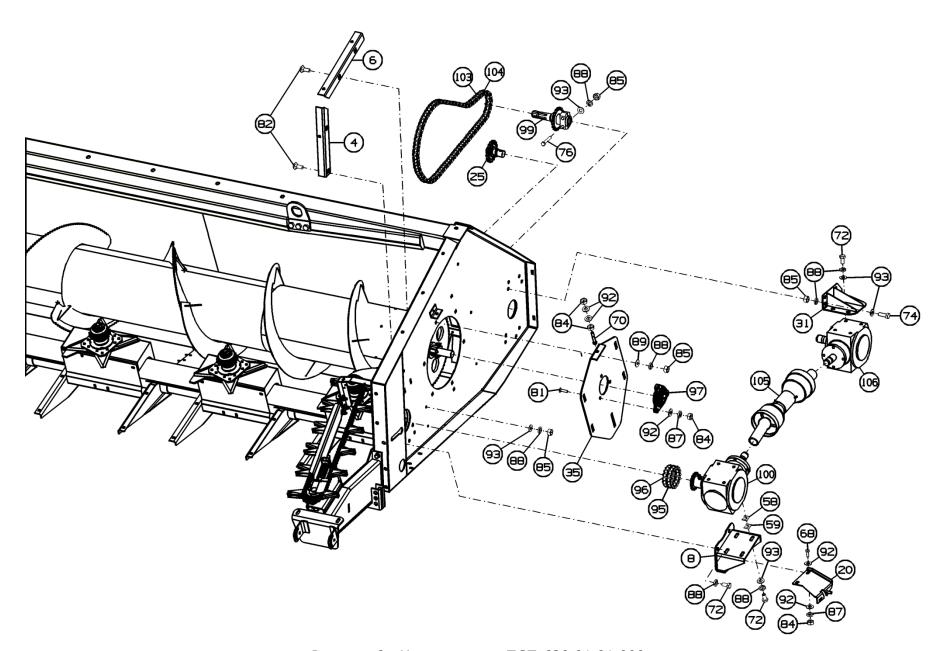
Корпус жатки ПСП-620.01.01.000
